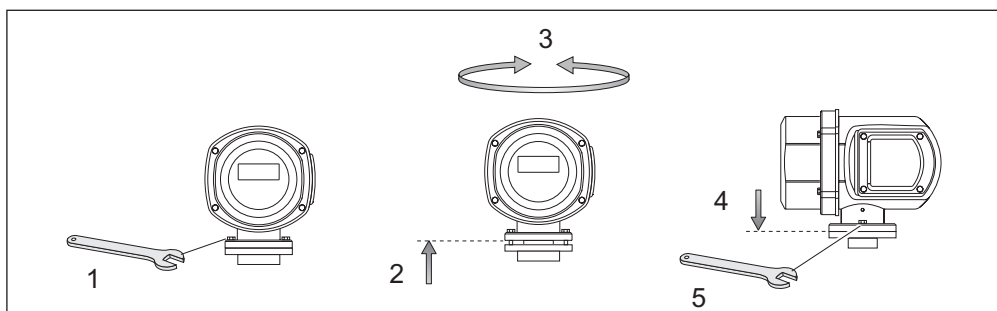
Вращение корпуса трансмиттера (полевой корпус из нержавеющей стали)
